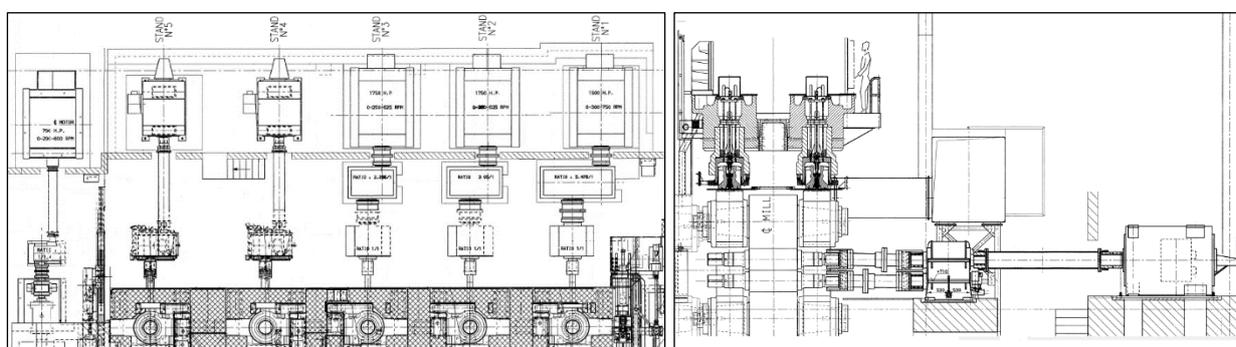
Vista de planta de zona transmisión (Reductores) y vista en corte de marcos 4 o 5.
